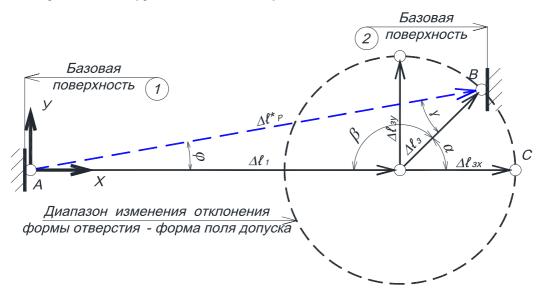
Модель размерной цепи, учитывающая положение и форму отверстий
